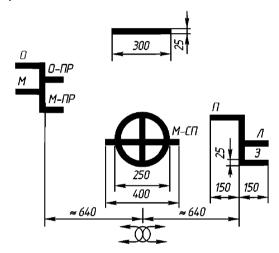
Общий вид и размеры знака грузовой марки
